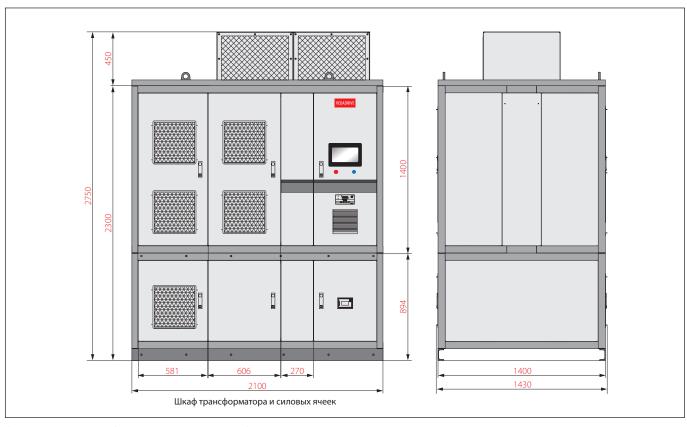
Корпус RA01 на напряжение 6 кВ
